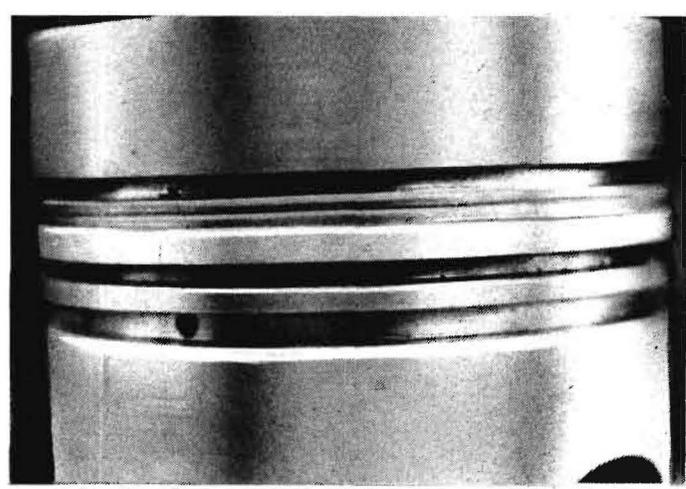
Umgeformter Ringträgerkolben MWH 1605 (R)
